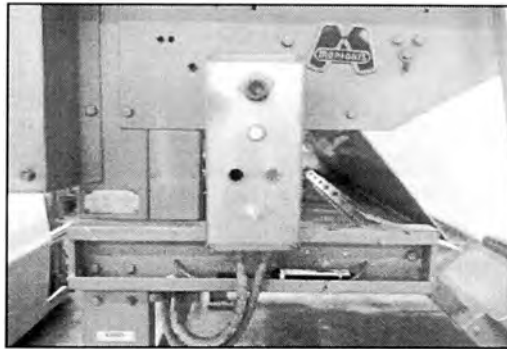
MANDO REMOTO EN EL ENROLLADOR
